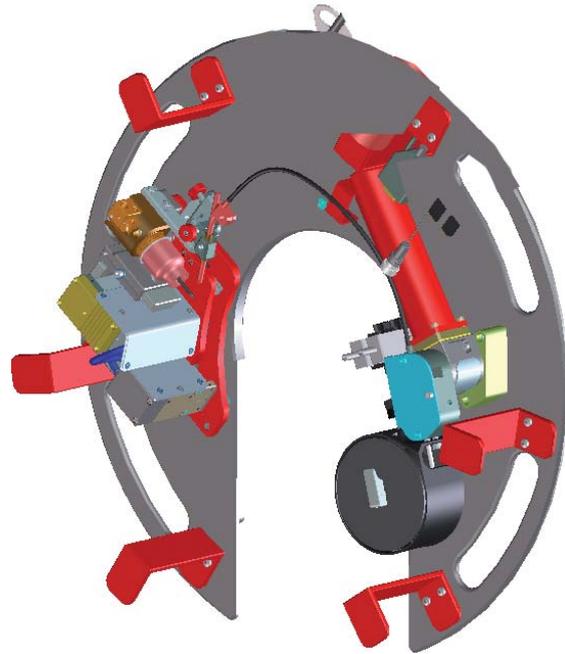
Werkzeugplatine MU IV 195 HW
